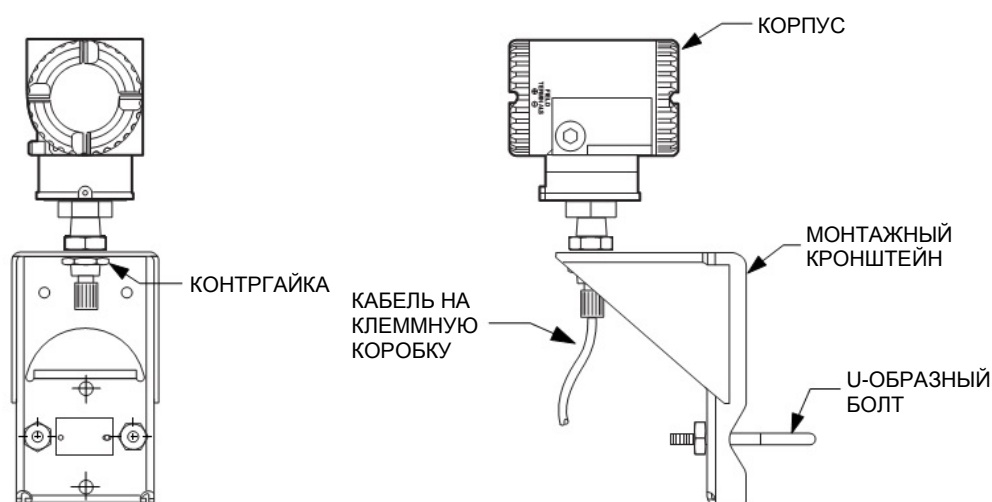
Раздельный монтаж корпуса модуля электроники
